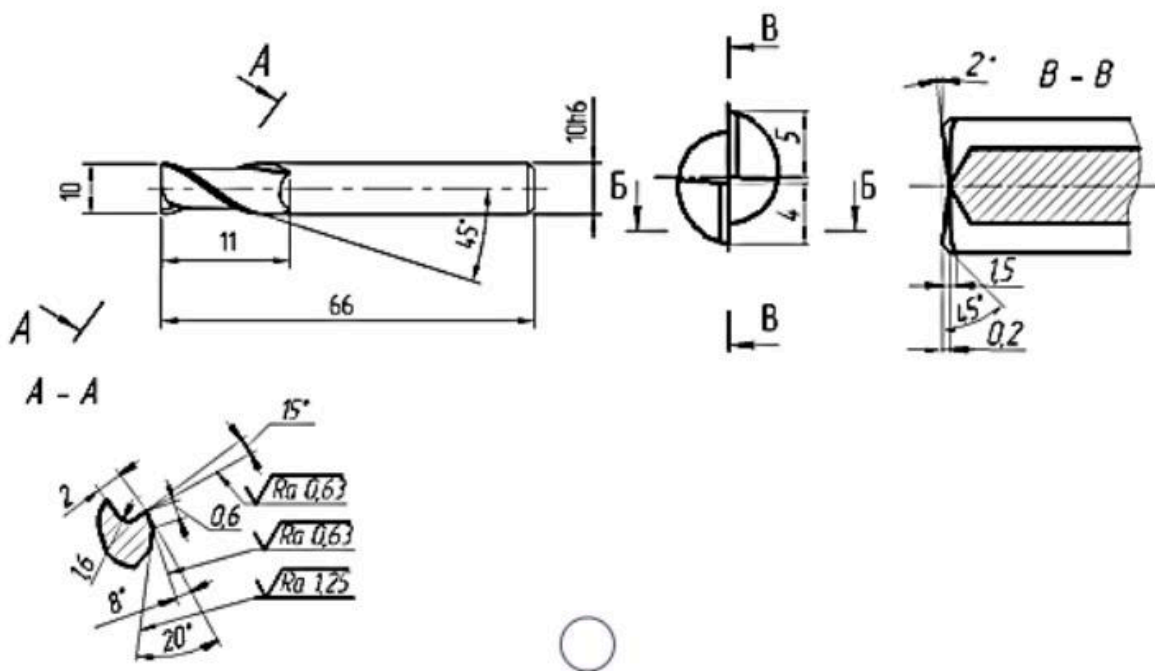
Эскиз с размерами опытной фрезы для обработки титанового сплава ВТ6
